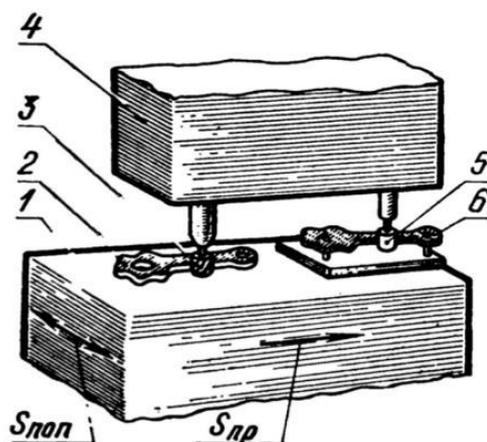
Принцип работы копировально-фрезерных станков
